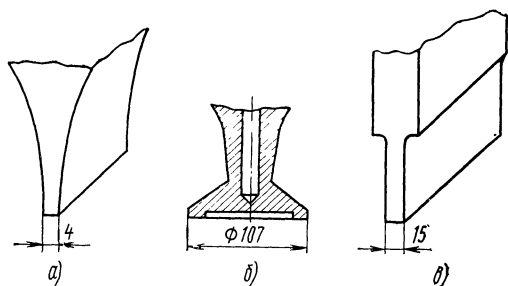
Ультразвуковые инструменты для сварки пластмасс
